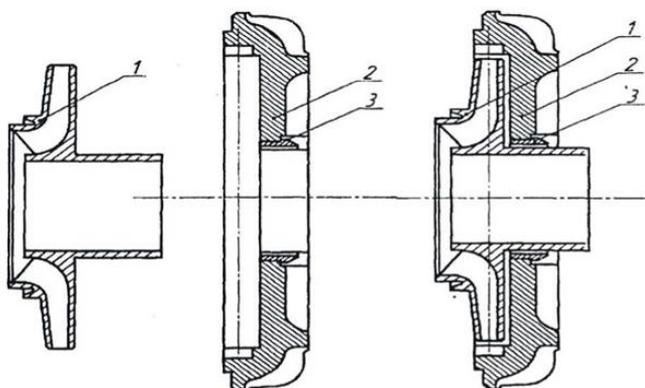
Элементы ступени и ступень в сборе 1 - рабочее колесо; 2 - направляющий аппарат; 3 – уплотнительное кольцо
